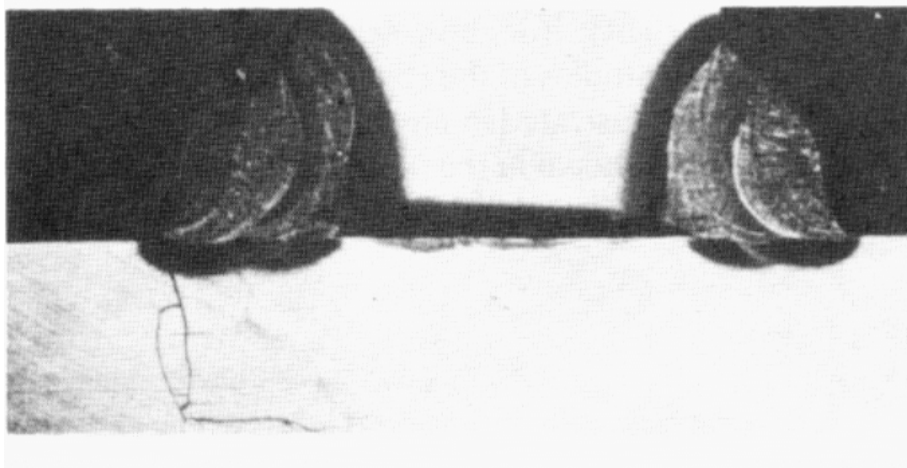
Corte de soldaduras de filete donde pueden observarse la presencia de fisuras
